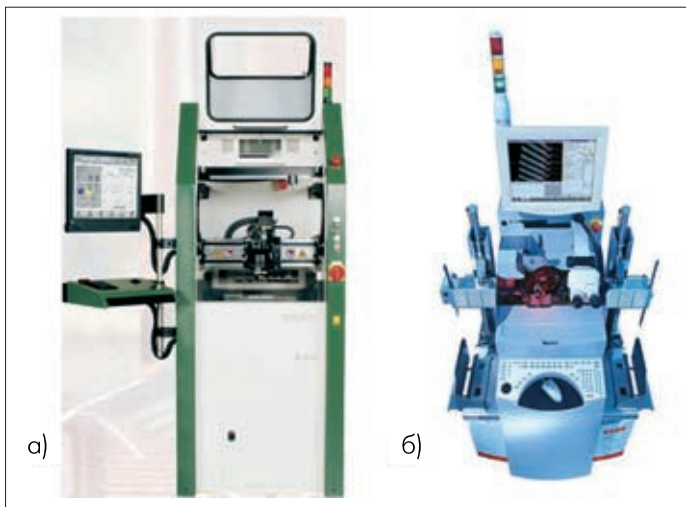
Автоматическое оборудование для клиновой и шариковой микросварки: а) установка клиновой сварки (модель VJ820); б) установка шариковой сварки (модель WB3100)
